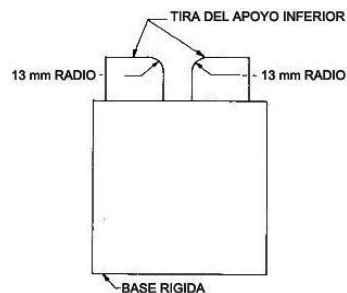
Detalle de la Tira Inferior de Apoyo
